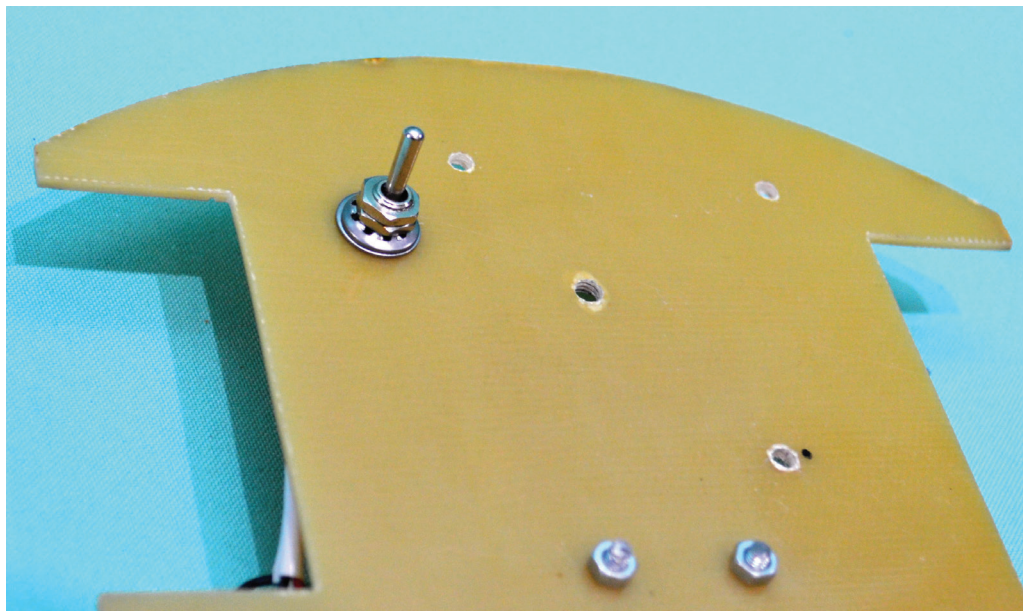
Выключатель установлен в отверстие корпуса (вид сверху)
